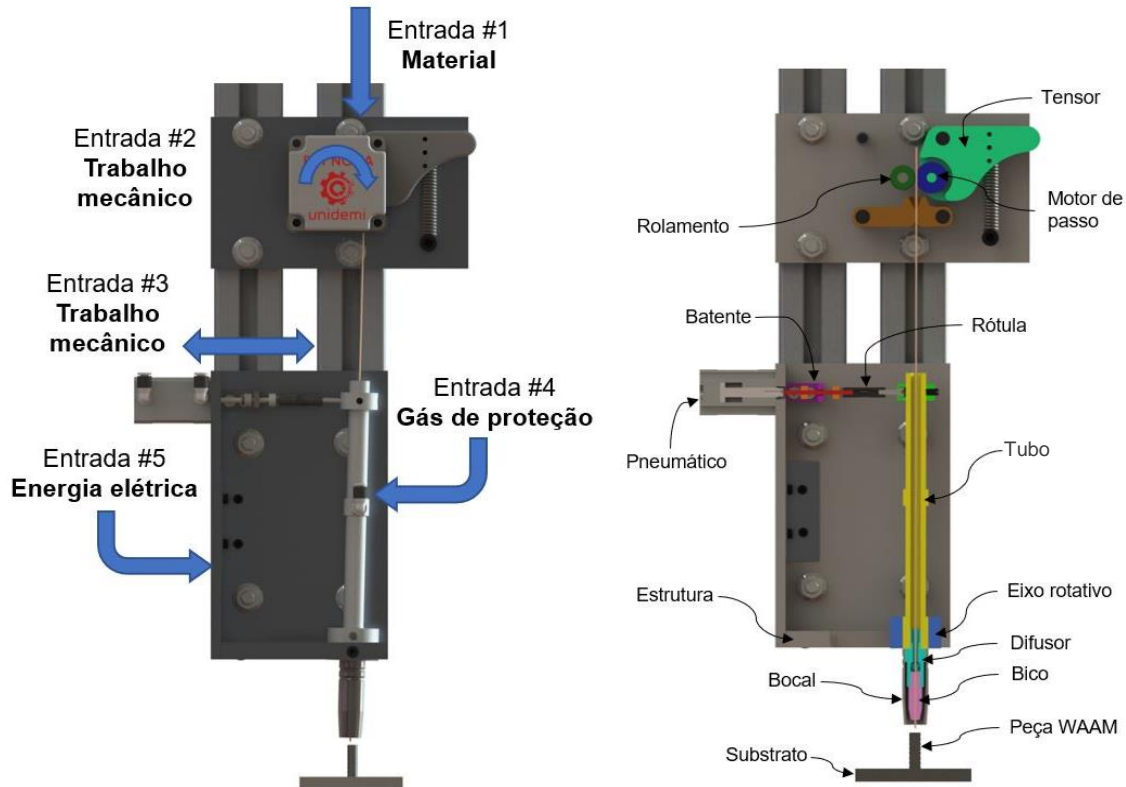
Vista frontal e vista de corte da Tocha WAAM.
